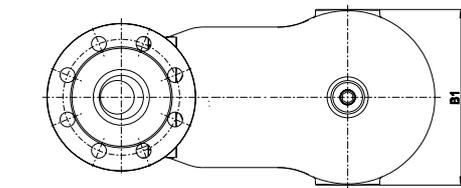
1 mit Flanschen - vertikale Einbaulage
